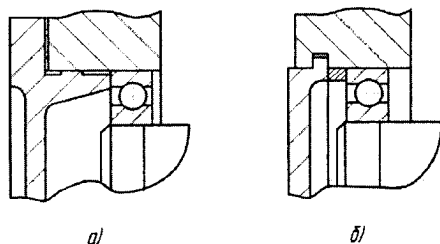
Види підшипникових кришок циліндричних редукторів
